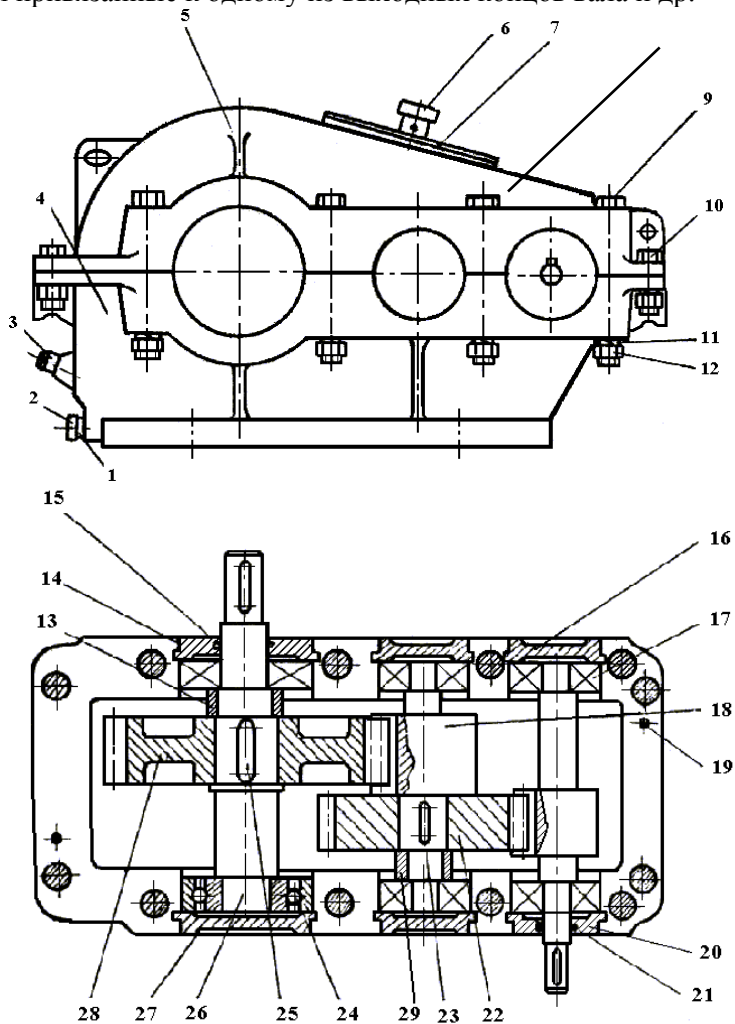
Цилиндрический двухступенчатый редуктор
